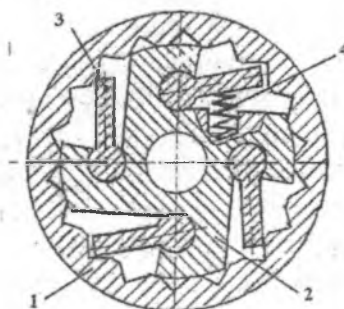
Поворотный механизм с двумя собачками в корпусе:
